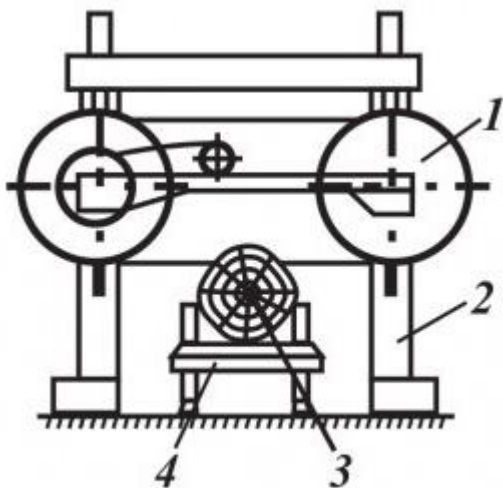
Схема стрічково-пилкового верстату для поздовжнього розпилювання колоди – горизонтального.
